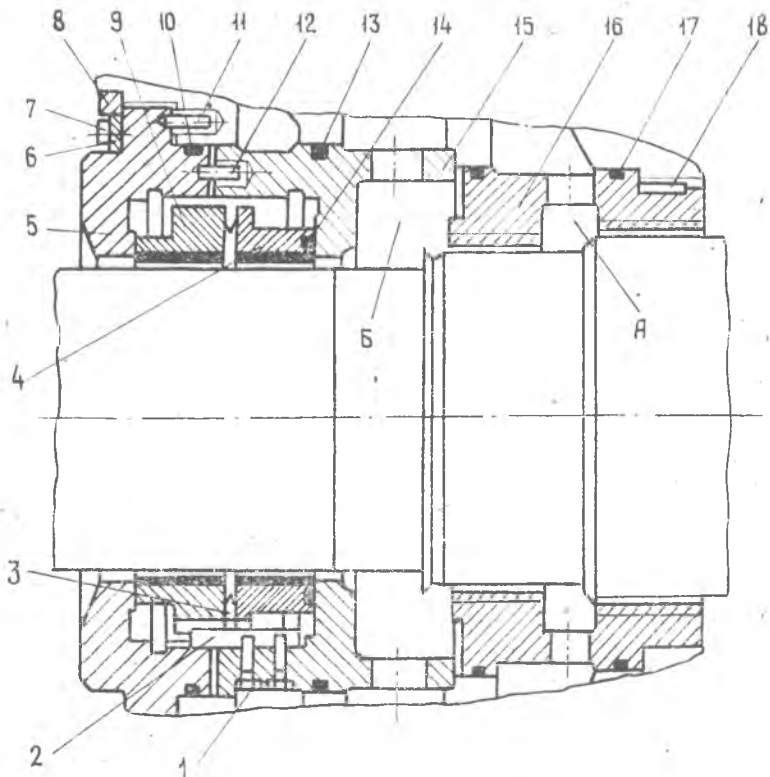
Уплотнение концевое: 1 — винт; 2 — шпонка; 3 — пружина; 4, 9 — кольцо; 5, 15 — корпус; 6 — планка; 7 — болт; 8 — кольцо разрезное; 10, 13, 14, 17 — кольцо уплотнительное; 11, 12 — штифт; 16 — втулка; 18 — шпонка
